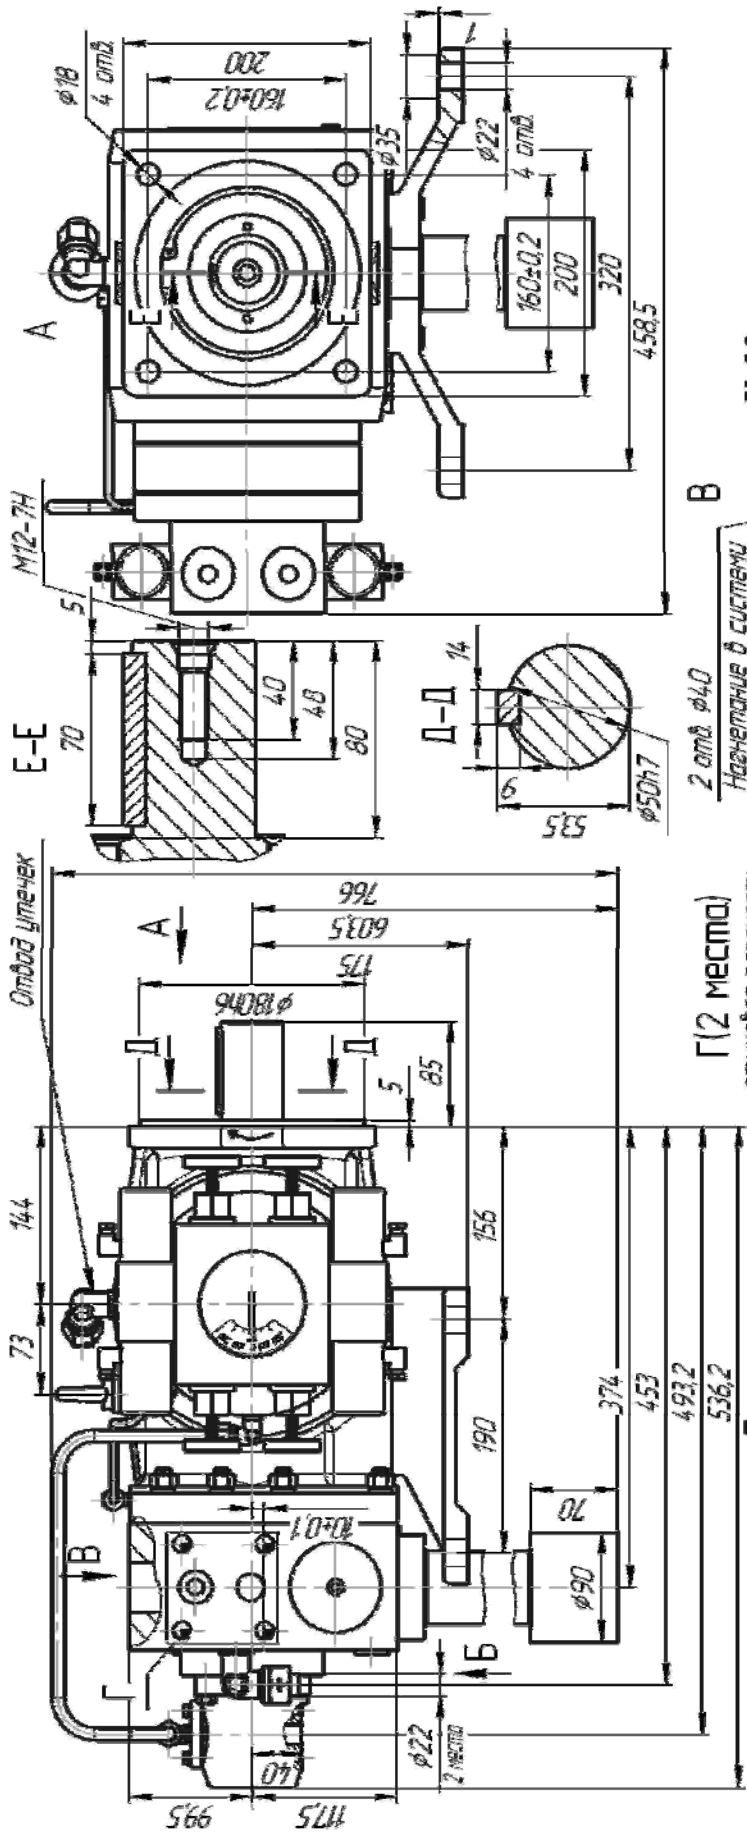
Габаритные и присоединительные размеры агрегата насосного АНЭ140/20
